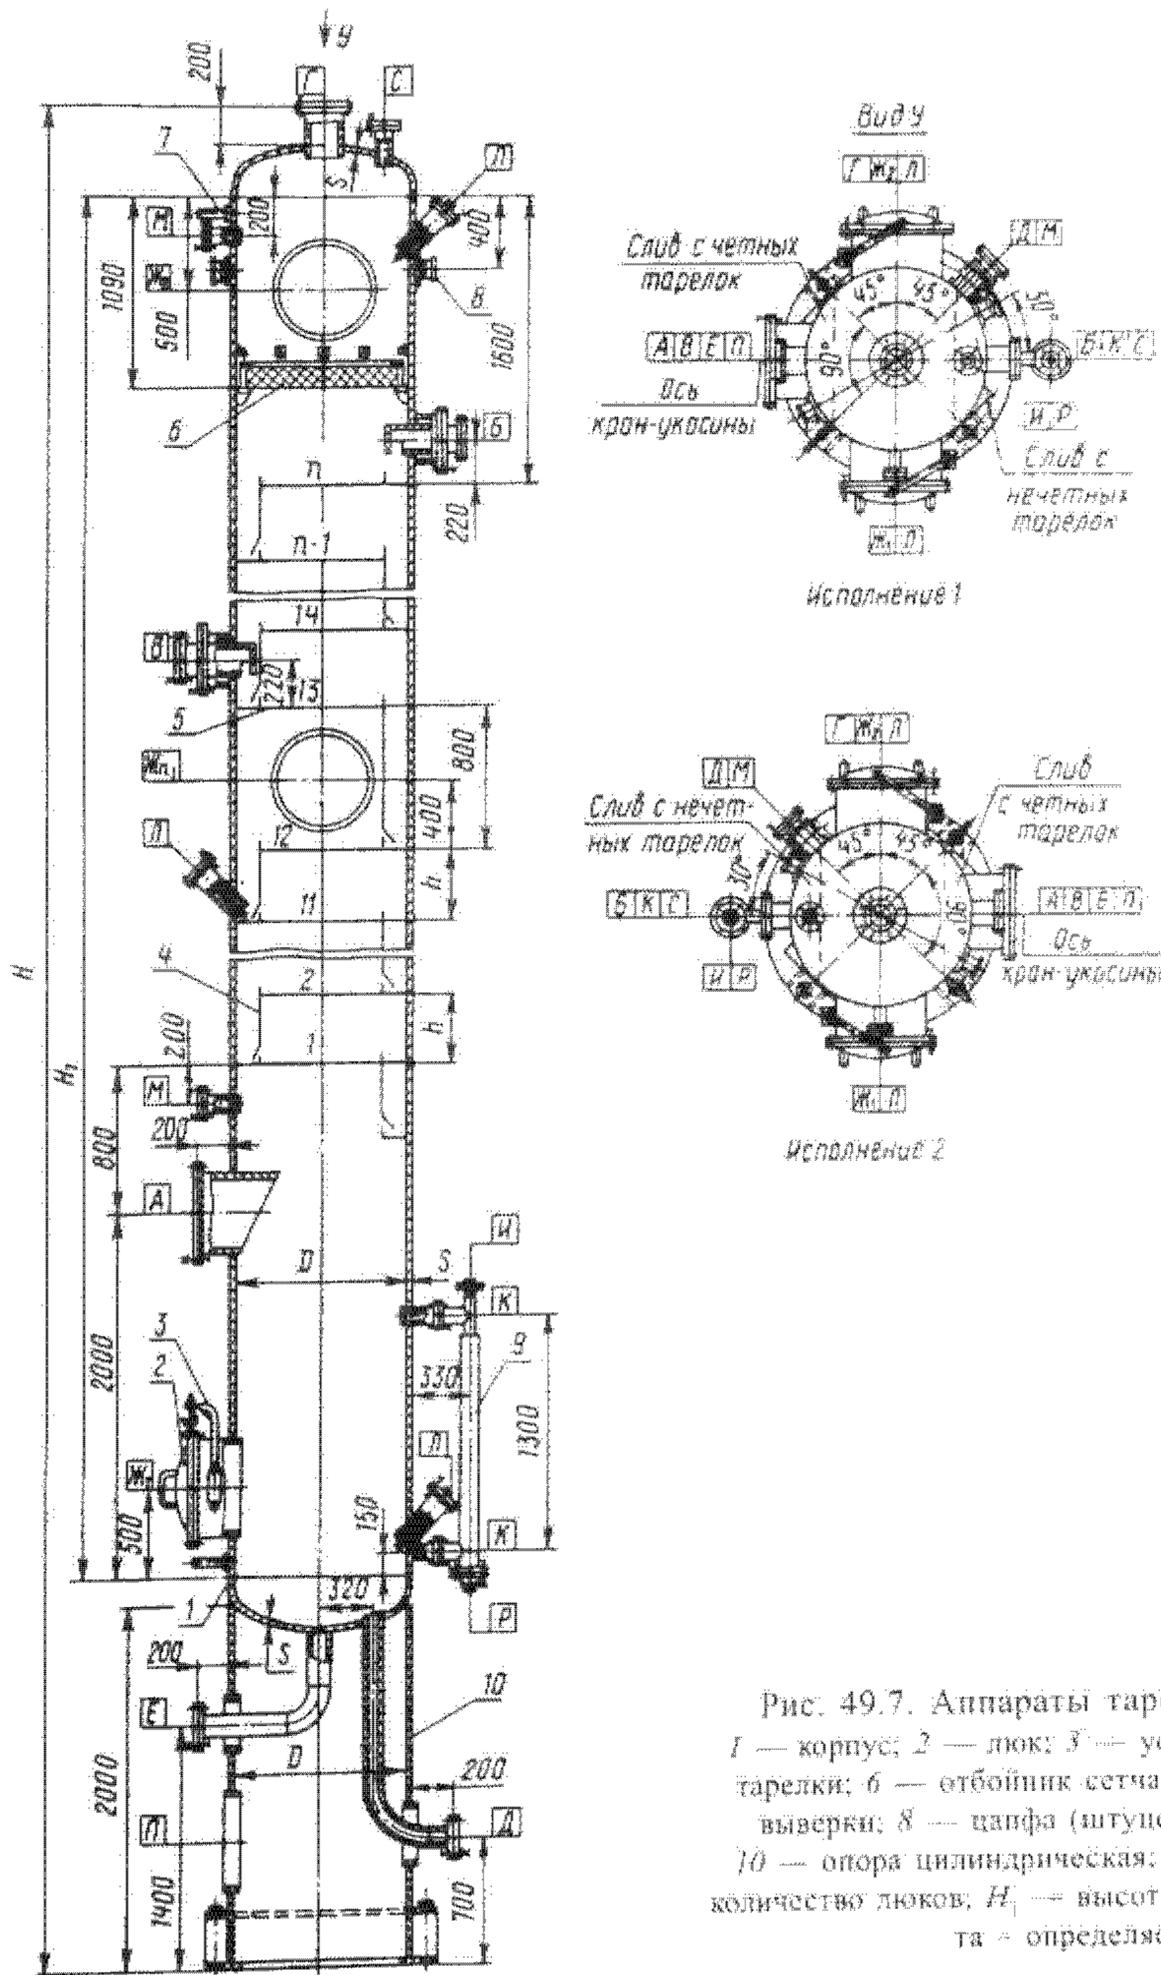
Аппараты тарельчатые цельносварные: 1 — корпус; 2 — люк; 3 — устройство поворотное; 4 и 5 — тарелки; 6 — отбойник сетчатый; 7 — приспособление для выверки; 8 — цапфа (штуцер); 9 — камера уровнемера; 10 — опора цилиндрическая;  $n$  — количество тарелок;  $n_1$  — количество люков;  $H_1$  — высота цилиндрической части аппарата — определяется заказчиком
